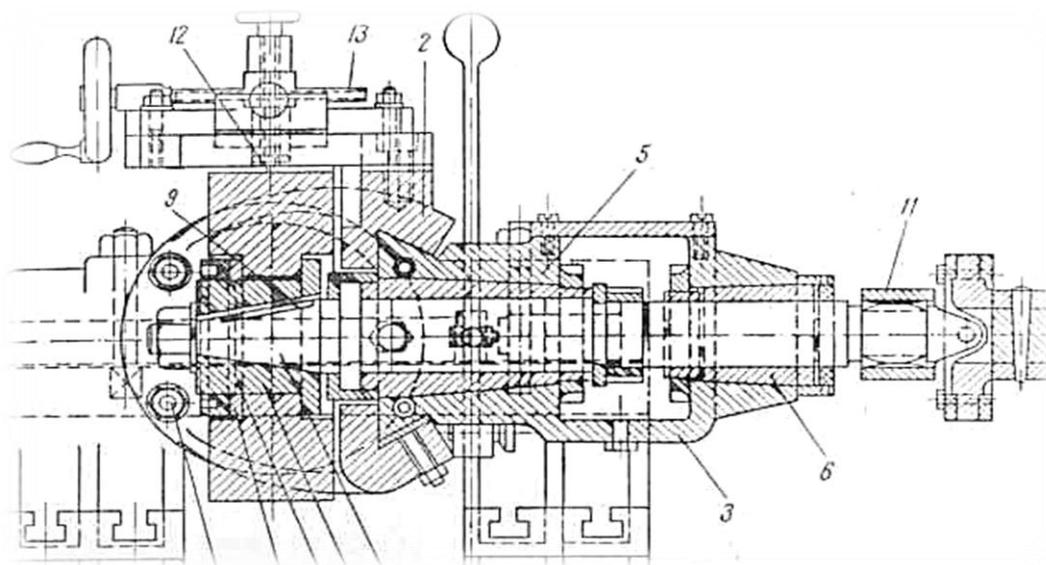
Приспособление для бесцентрового шлифования веретен
